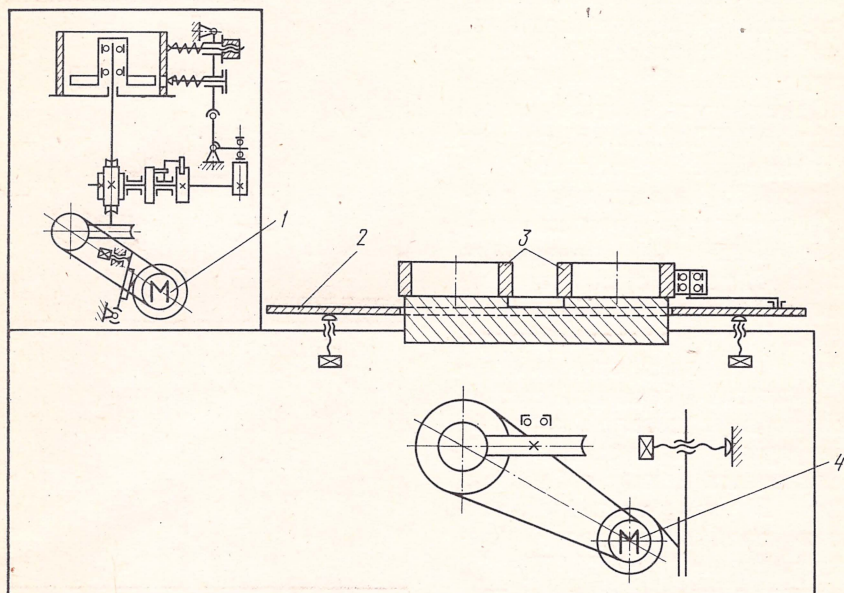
Кинематическая схема плоскодвоточного однодискового станка 3804П:
